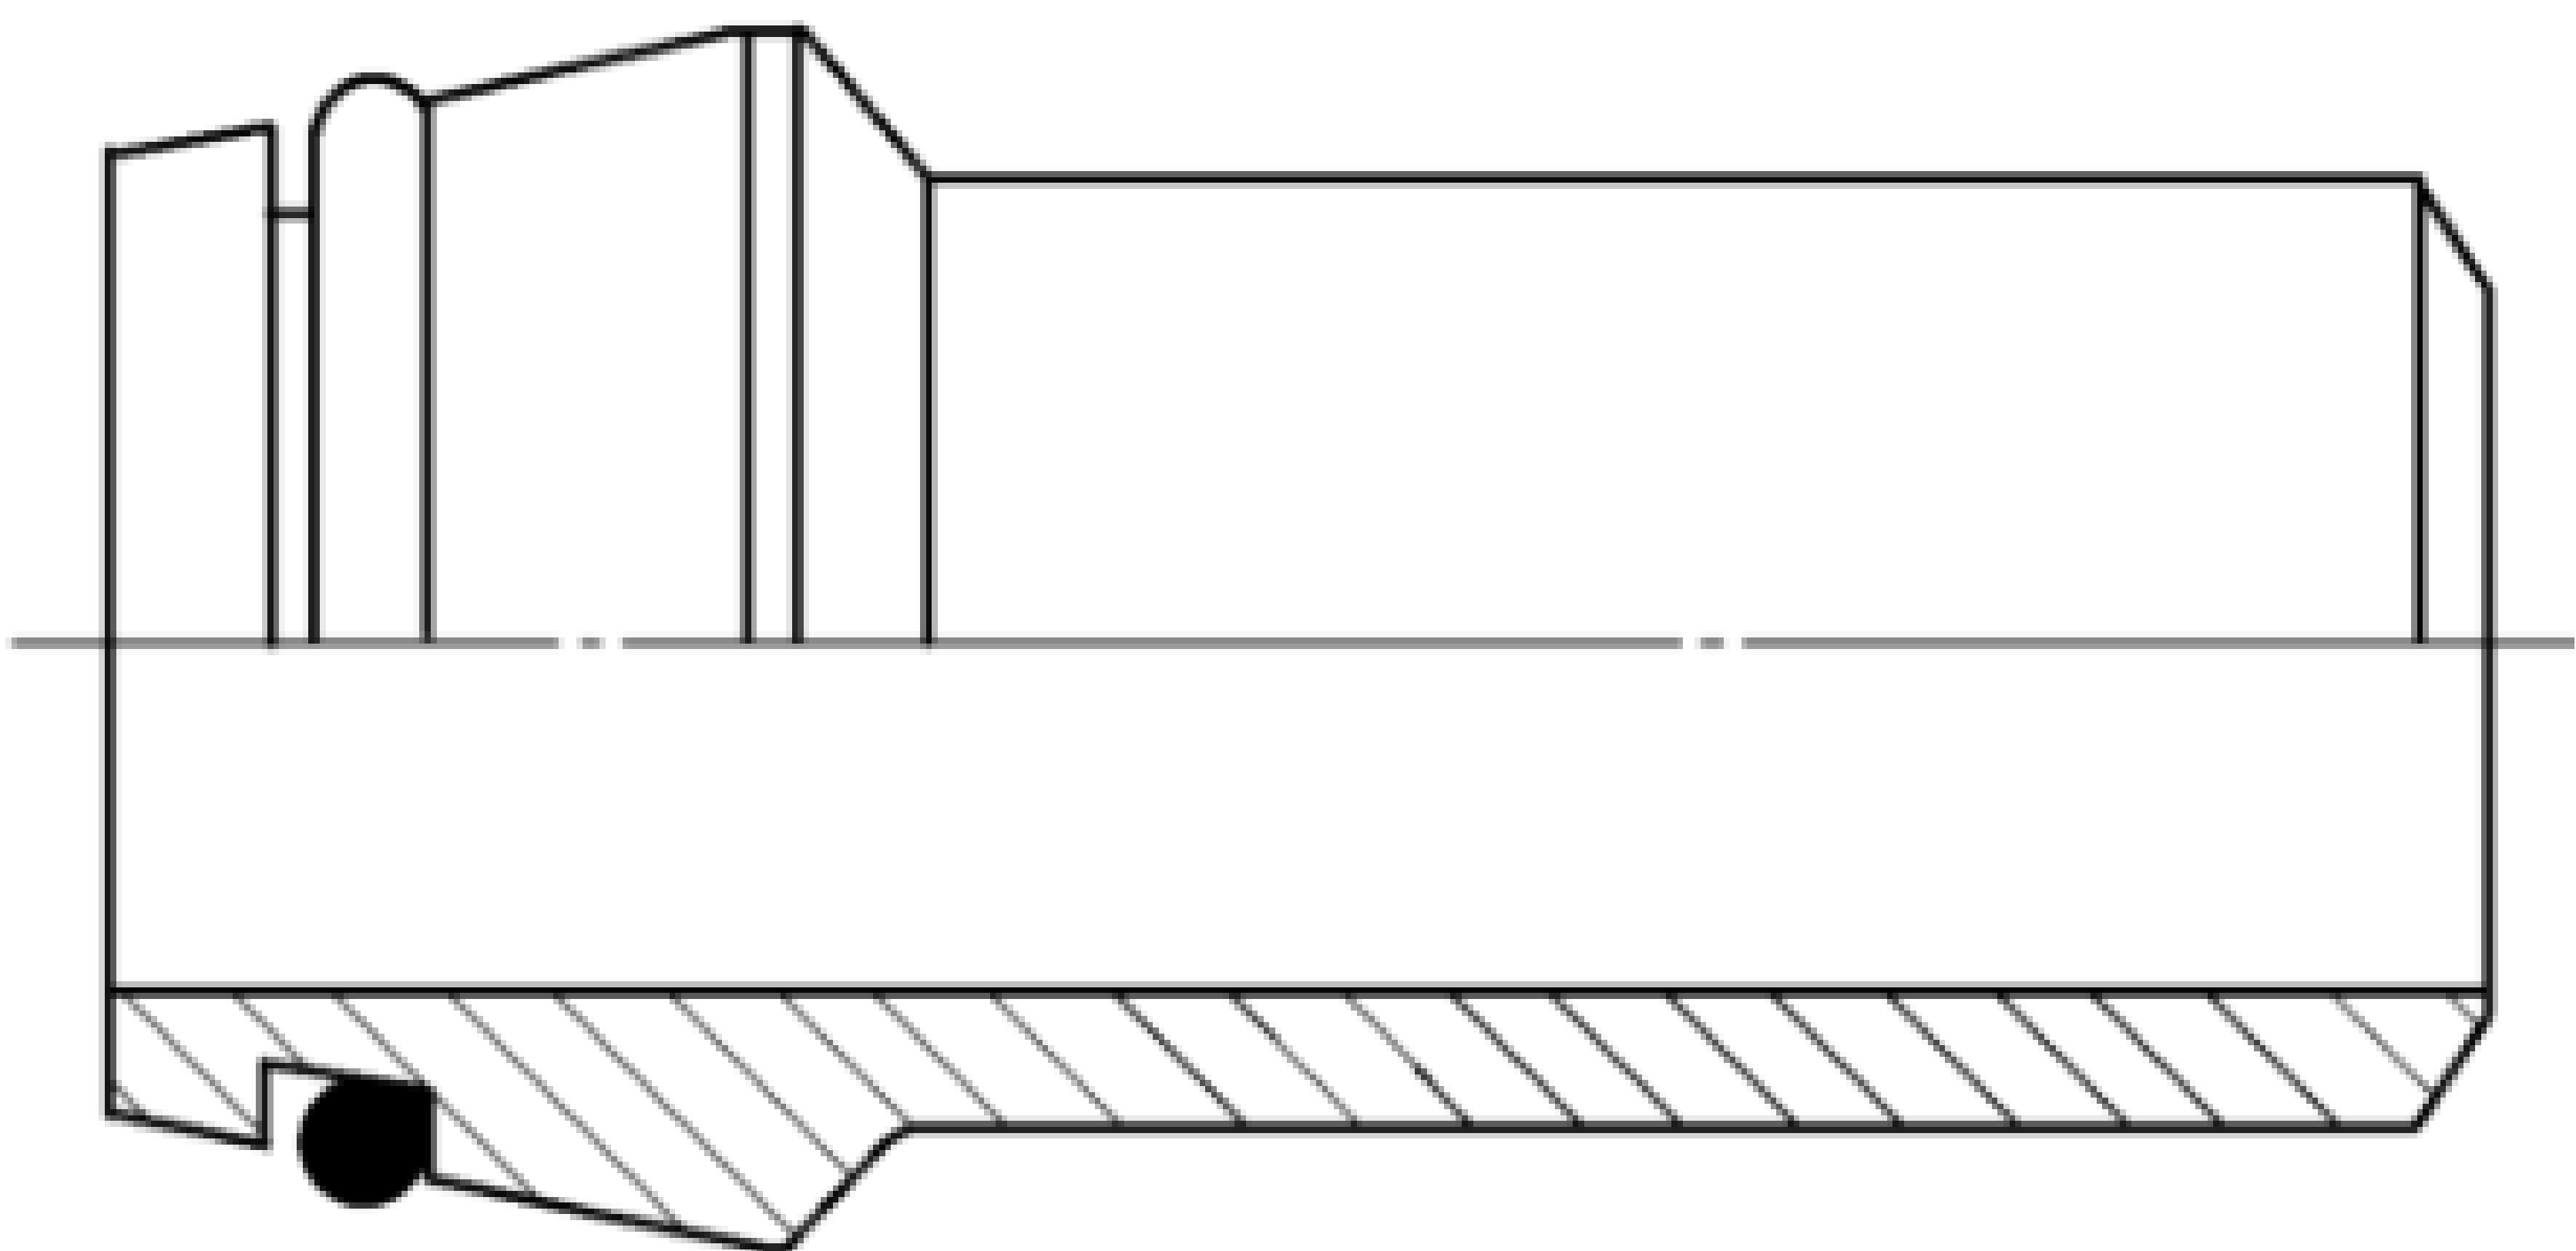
带 O 形圈的焊接接管(WDNP)
